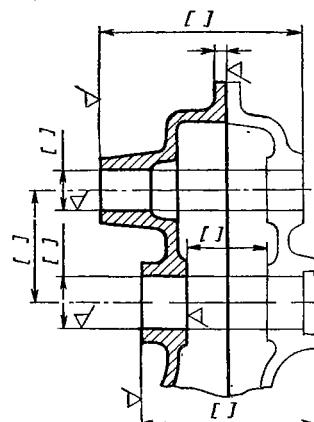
Нанесение размеров, связывающих две совместно обрабатываемые детали
